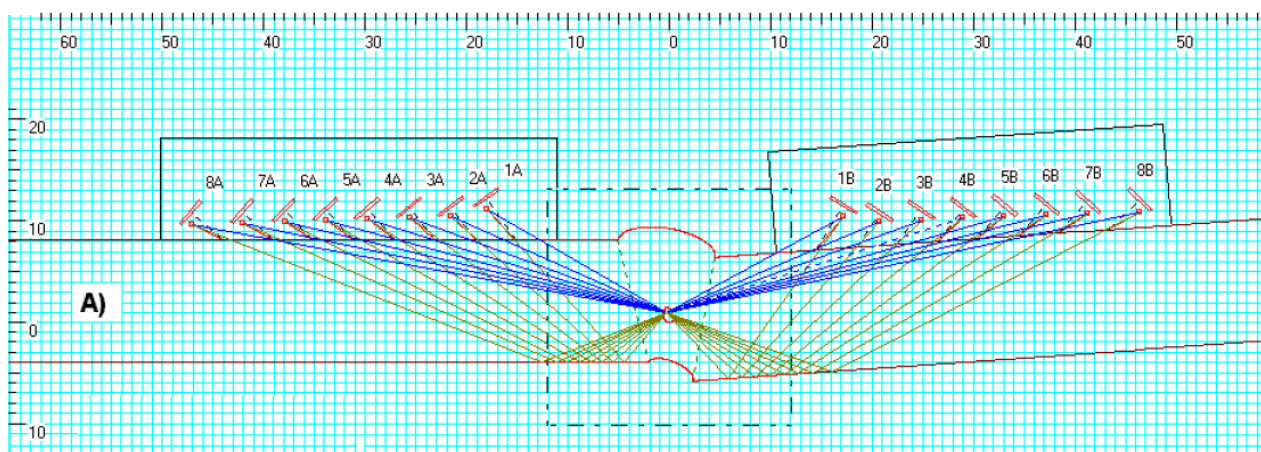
Контроль центральной области сварного соединения
